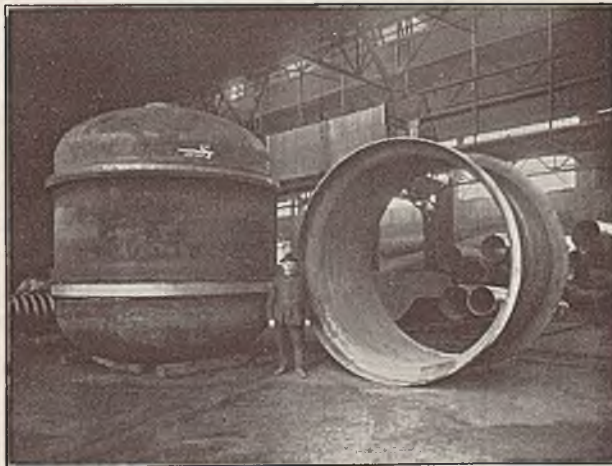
Dreiteil. Kabelträngef. 3250 mm l. Φ , 5987 mm ganze Höhe, 20 mm Blechstärke mit vorgeschweiß. Stahlgußflansch. Rechts geschw. und gebördelter Generatormantel von 2800 mm l. Φ , 3150 mm ä. Φ , 1710 mm Länge und 25 mm Blechstärke
